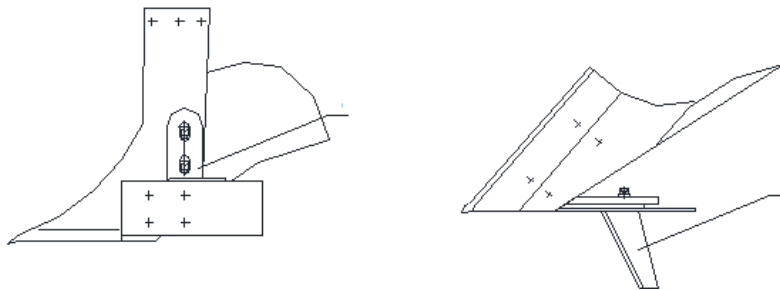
Пристрій установлений на корпусі плуга
